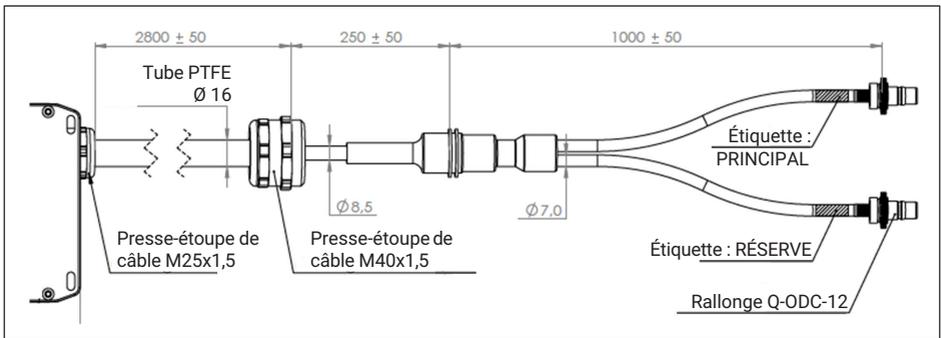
Boîtier d'interconnexion – Côté câble – Dessin technique (dimensions en mm)
